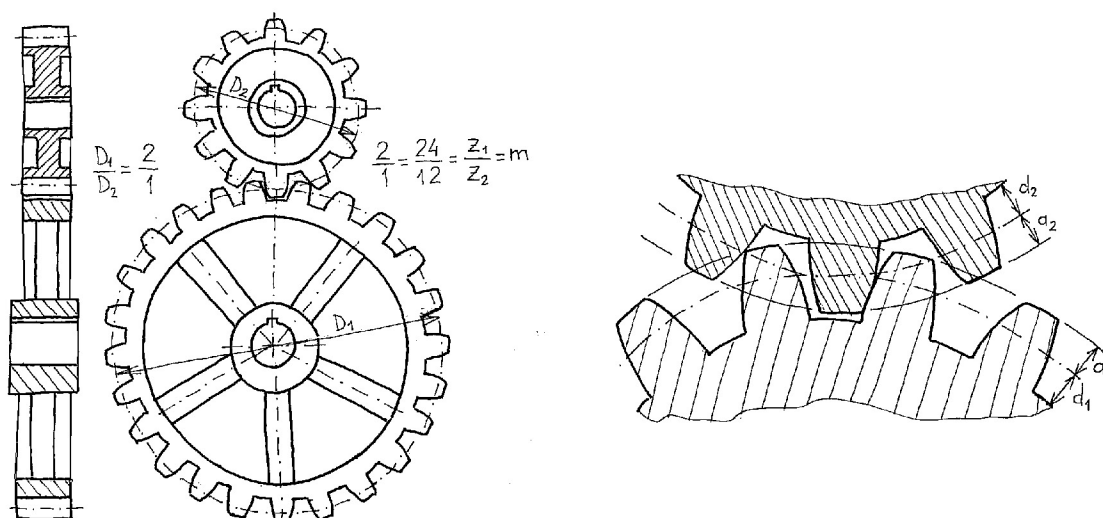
Engranaje de dos ruedas dentadas (izquierda) con detalle del contacto entre dientes (derecha)
